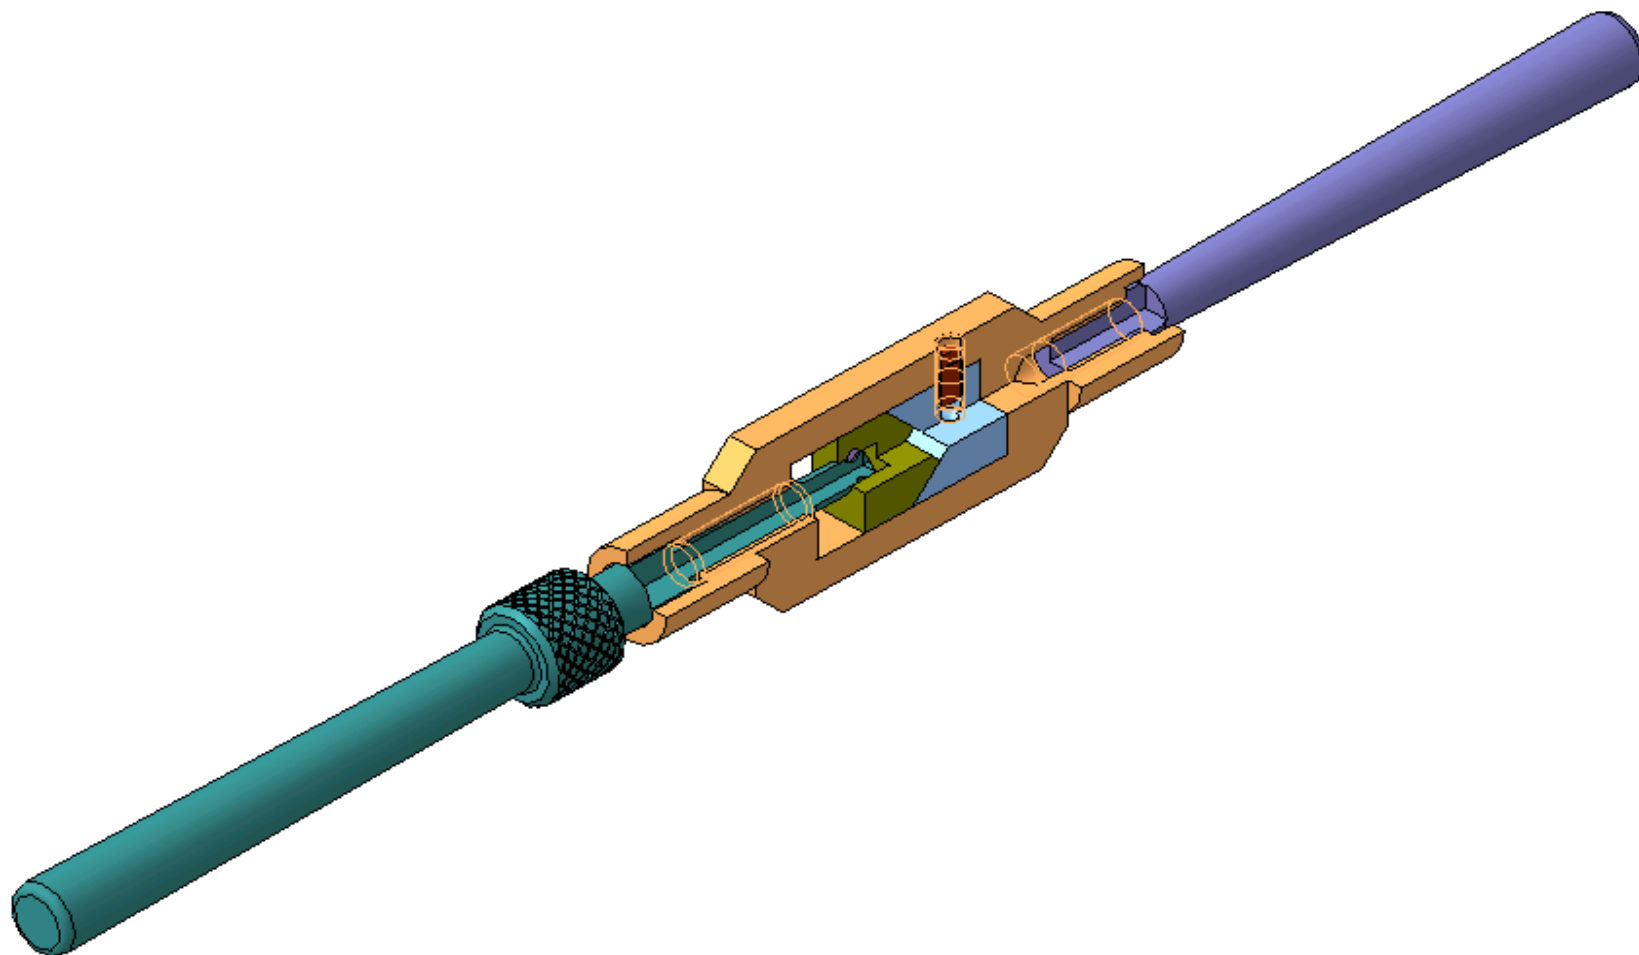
3D-модель сборки изделия «Вороток раздвижной» (варианты 10, 30)
